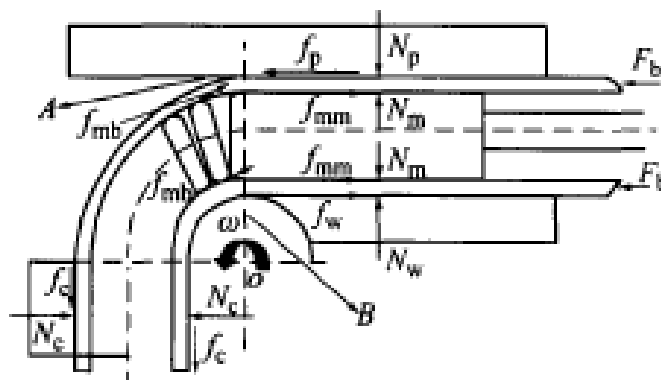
Fuerzas de presión y fricción que actúa en el doblado.
